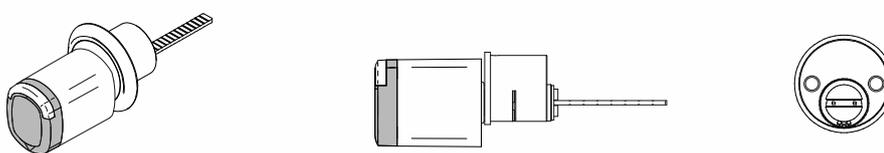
Профиль RIM. Полуцилиндр со считывающей головкой
